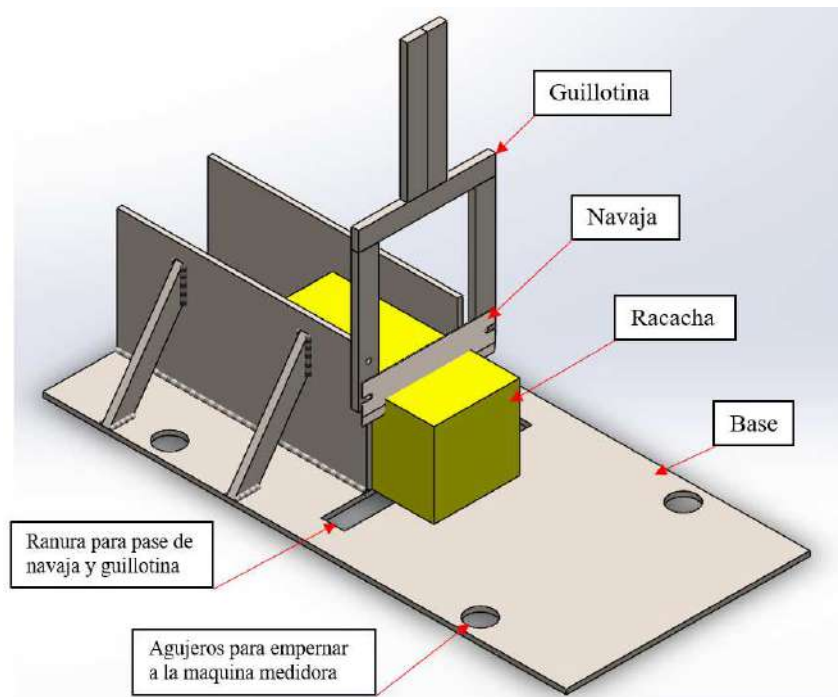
Montaje final de prototipo para corte de Racachas.
